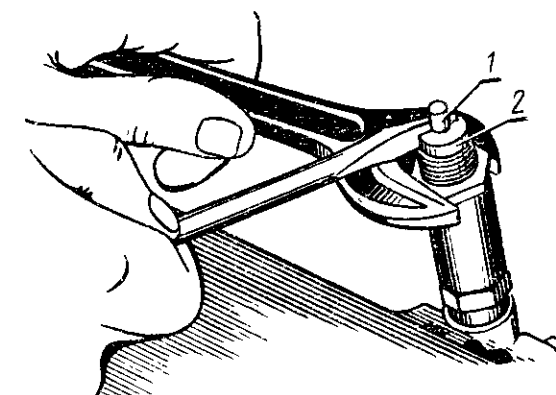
Регулировка предохранительного клапана пневмосистемы:
